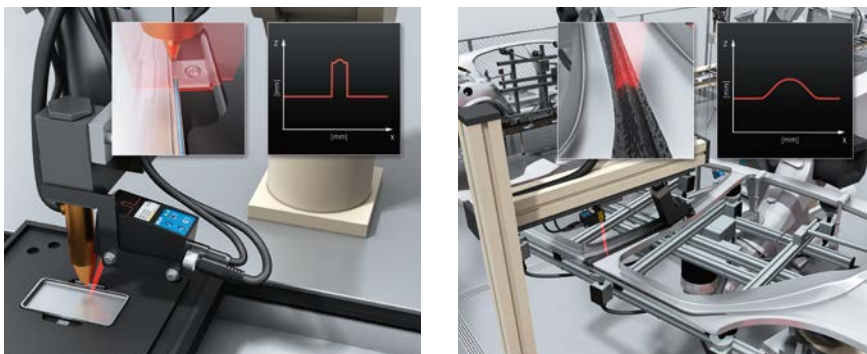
Inspección sin contacto del cordón de masilla adhesiva en un proceso continuo con el sensor de desplazamiento Profiler 2
